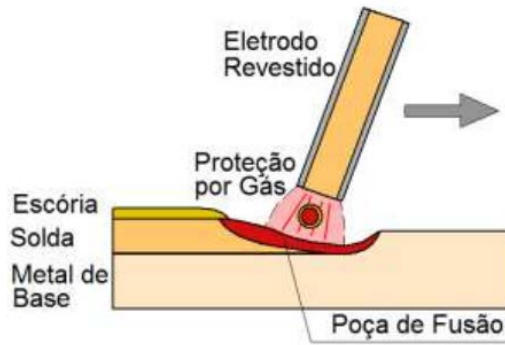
Esquema da soldadura por eletrodo revestido [53]
